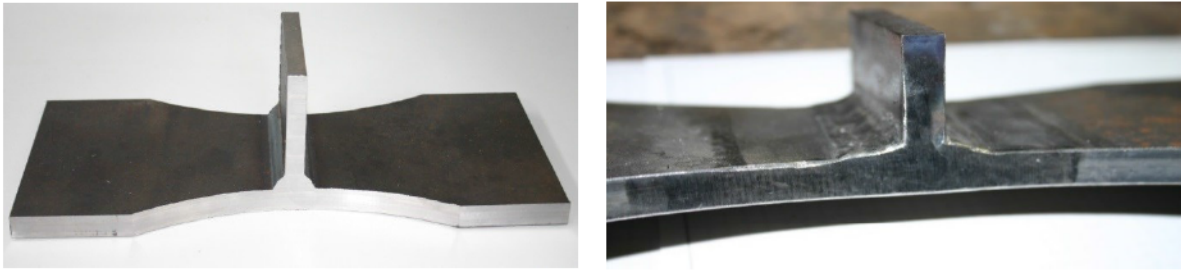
Ansicht auf die Schweißnähte im geschweißten Zustand (li.) u. nach der Sanierung (re.)
